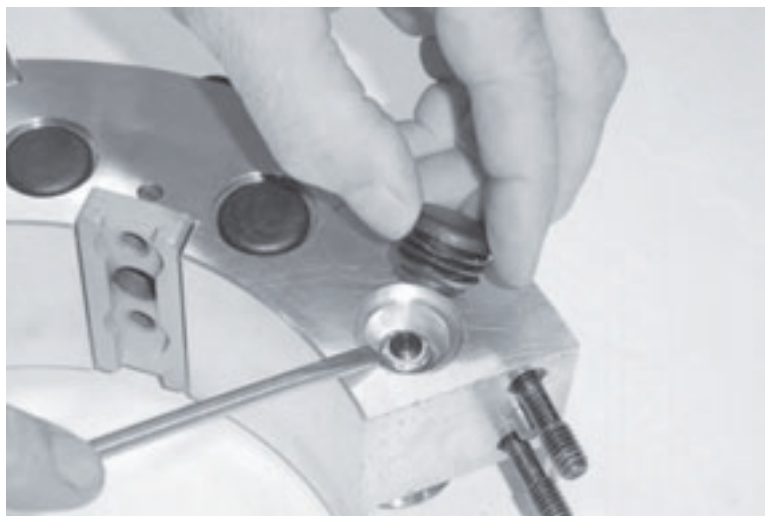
Снимите пластмассовые колпачки для осмотра подшипниковых узлов.
